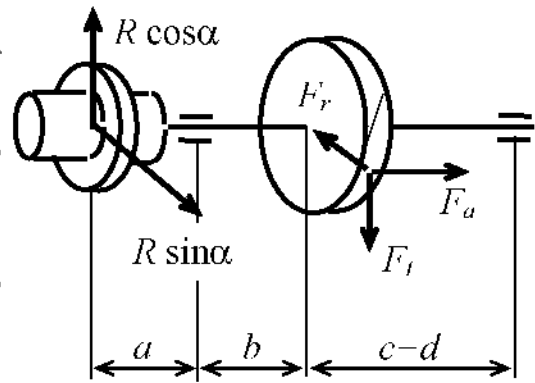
Схема нагружения тихоходного вала редуктора
